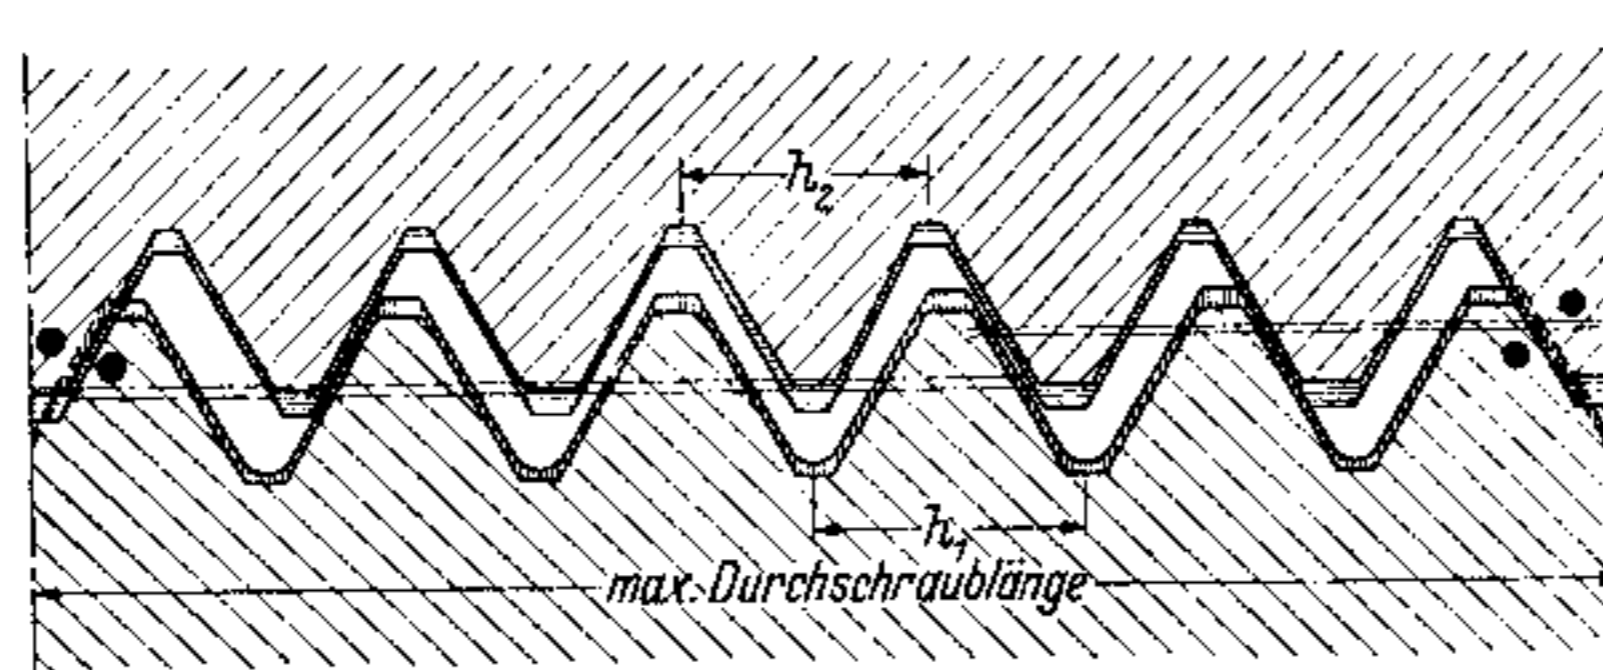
Bekannte Ausführungen von Schrauben mit Differentialgewinde.
